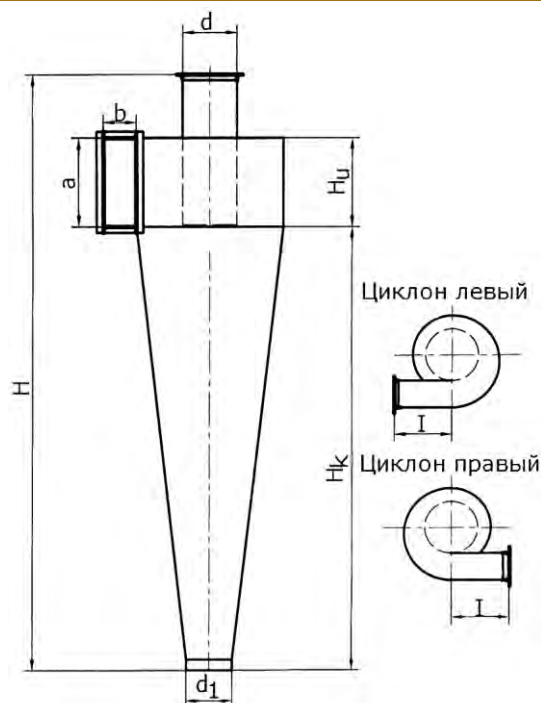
Габаритные и присоединительные размеры циклонов СК-ЦН-22.
